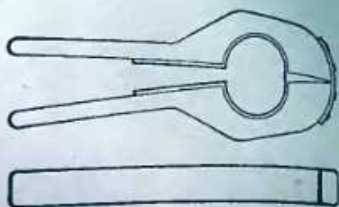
Жимки ЛМ9666-089 для полировки шеек колесчатого вала
